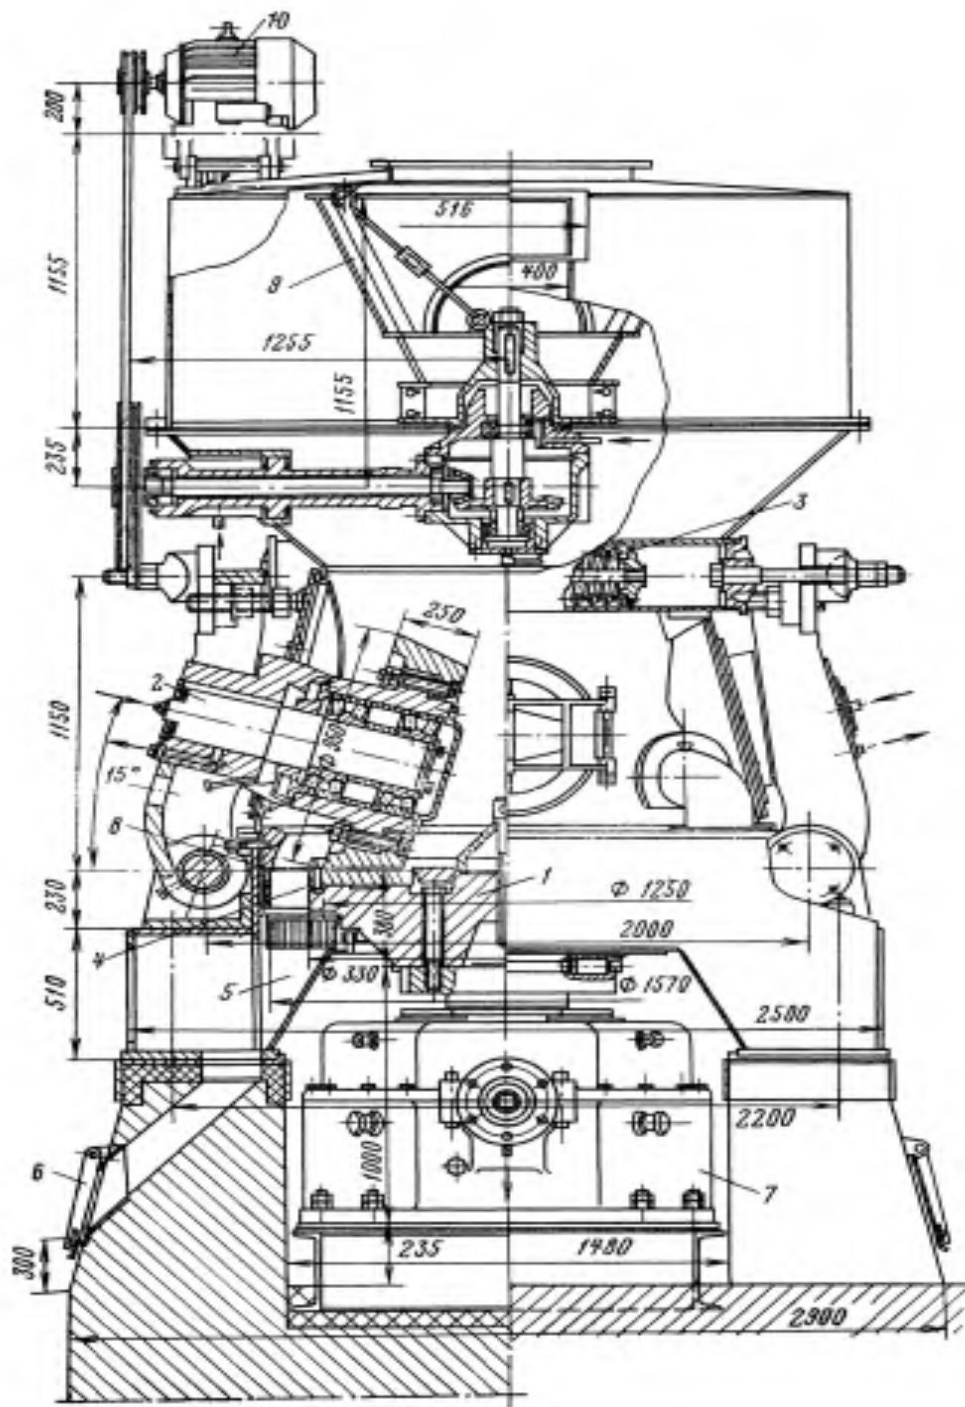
Среднеходная валковая мельница (МВС): 1 – размольный стол; 2 – мелющий валок; 3 – нажимная пружина; 4 – подпорное кольцо; 5 – воздушный короб; 6 – карман для отхода; 7 – редуктор; 8 – кольцевой канал; 9 – вращающийся сепаратор; 10 – электродвигатель привода сепаратора
